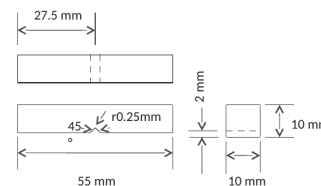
Dimensiones de las probetas de impacto Charpy según ASTM E-23.
